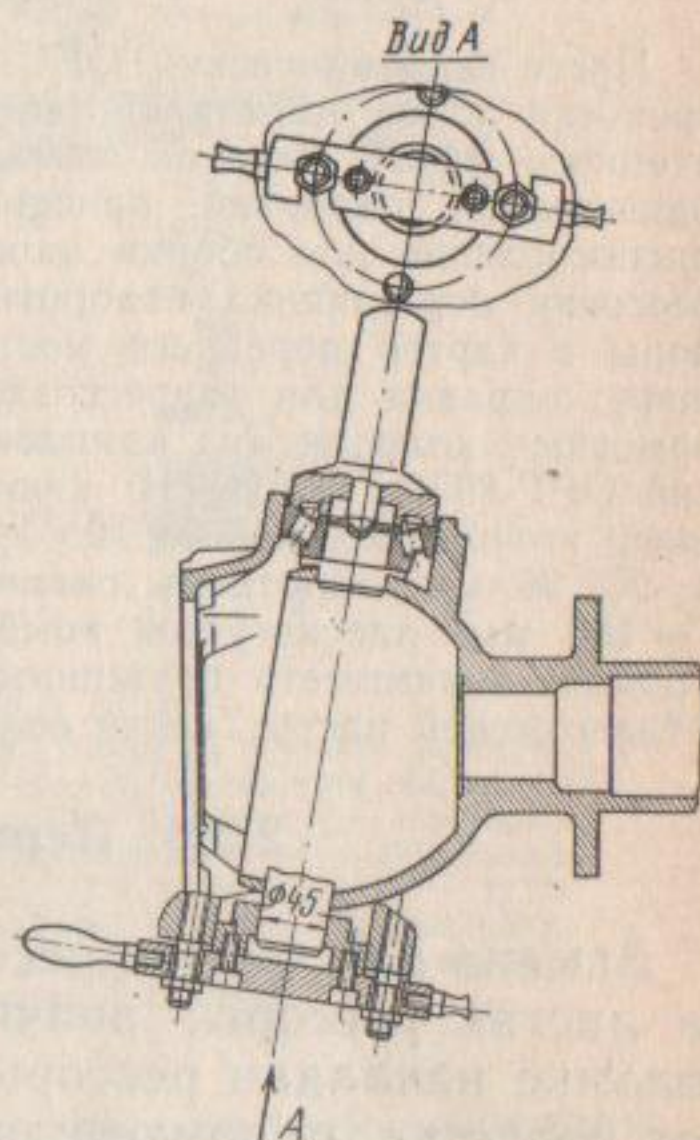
Общий вид приспособления для запрессовки подшипника поворотного кулака
